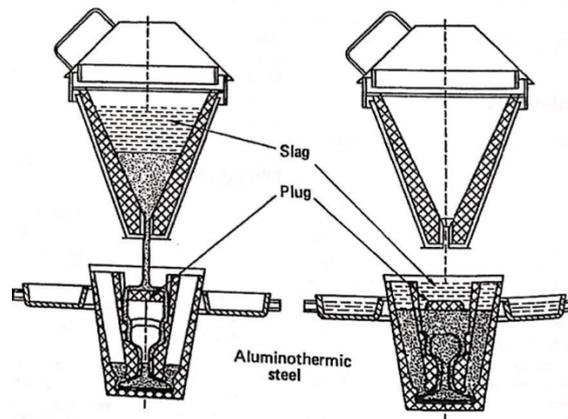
Soldadura aluminotérmica de carriles (slag: escoria, plug: tapón refractario diversificador del caldo; aluminothermic steel: acero aluminotérmico).
